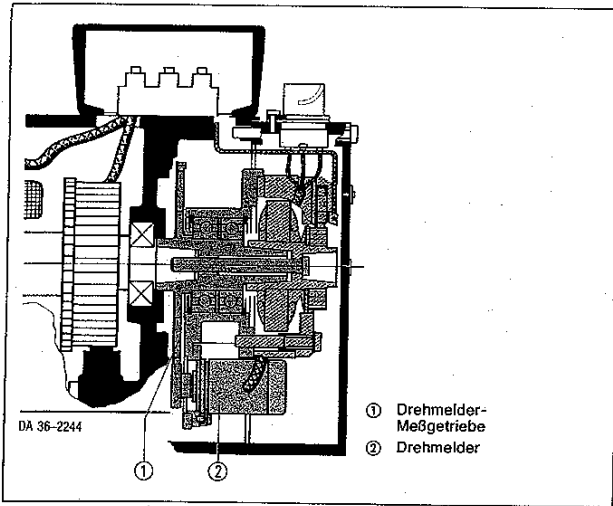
/12 Vorschubmotor mit eingebautem Drehmeldermeßgetriebe
